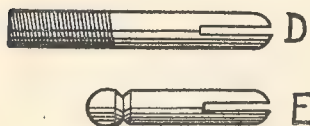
Die Bolzen, zwischen die das Metallband eingespannt wird.
